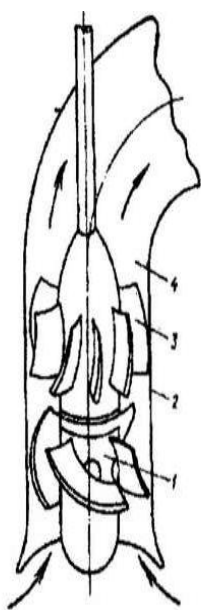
Схема конструкции осевого насоса: 1 - рабочее колесо; 2 - корпус; 3 - направляющий аппарат; 4 - трубопровод
